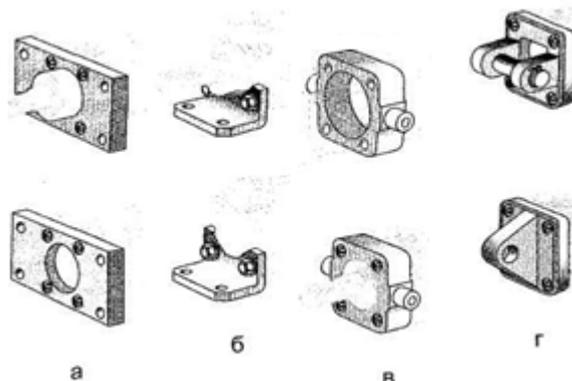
Элементы крепления пневмоцилиндров:
